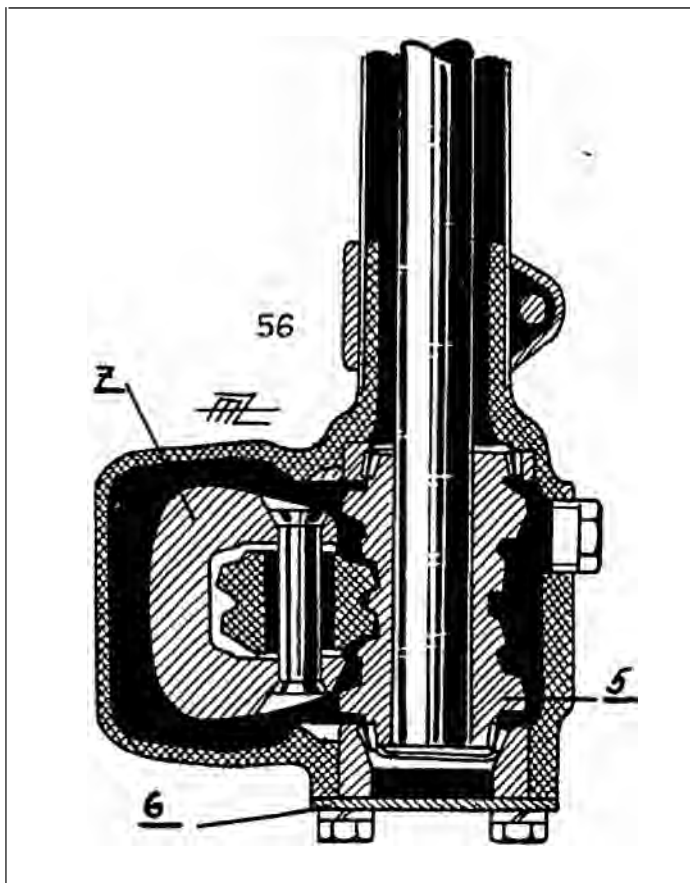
Coupe d'une direction à galet (Vue en élévation)
